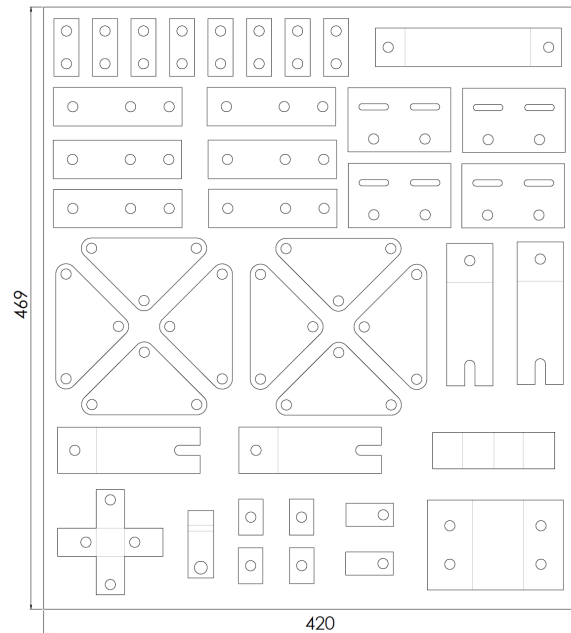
Plancha inicial para la fabricación de las piezas de hierro - Creado con InDesign por Álvaro Otero.
